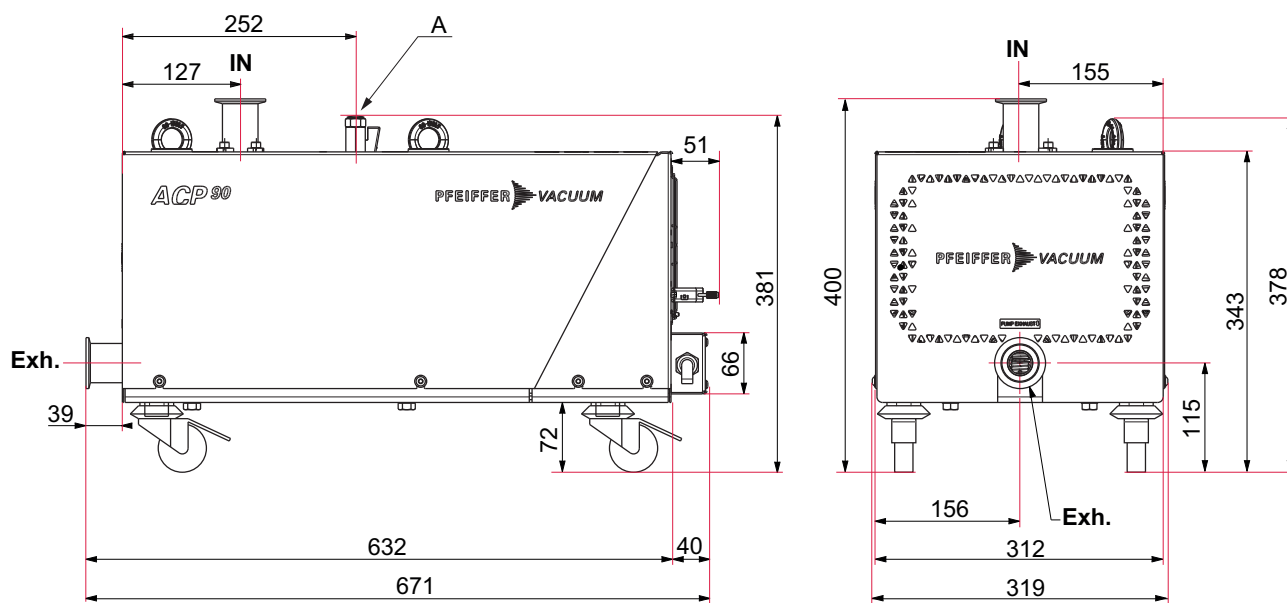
Abmessungen (mm) ACP 90 mit Rollen
